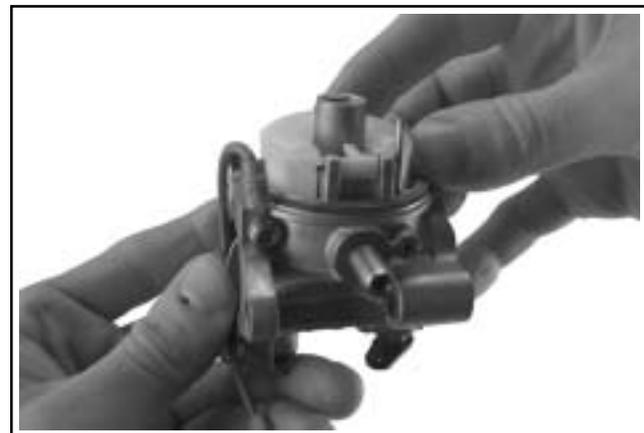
Installazione di galleggiante e spillo di ingresso del carburante.
